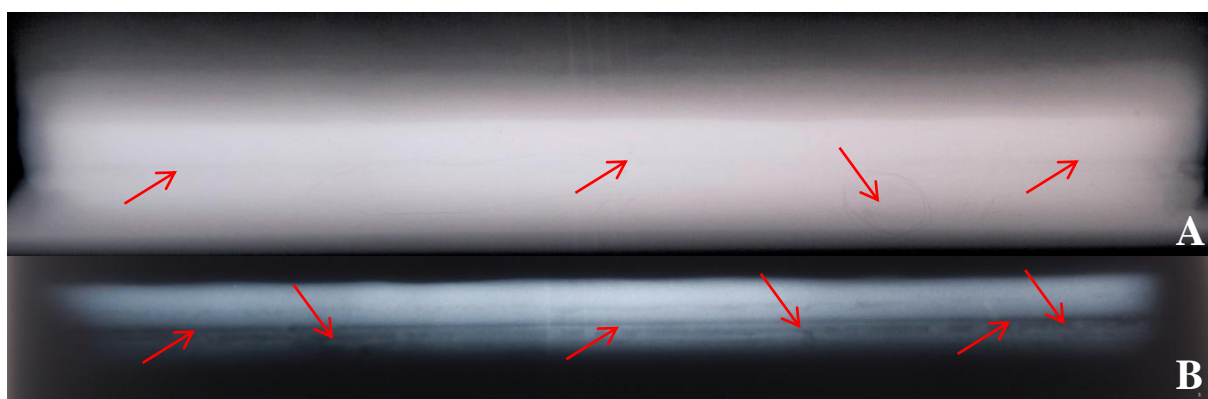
Radiografias do corpo de prova soldado com o processo FCAW
